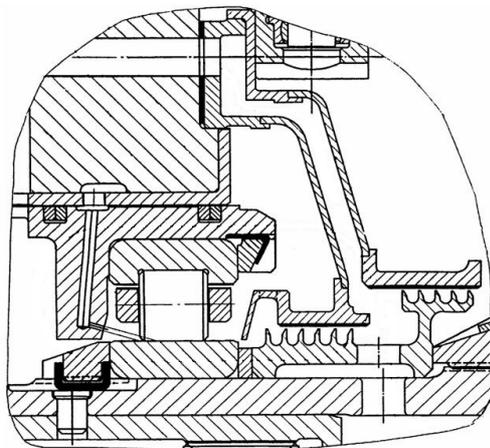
Подвод смазки к опоре ГТД через форсунку в зону контакта тел качения с нижней обоймой подшипника
